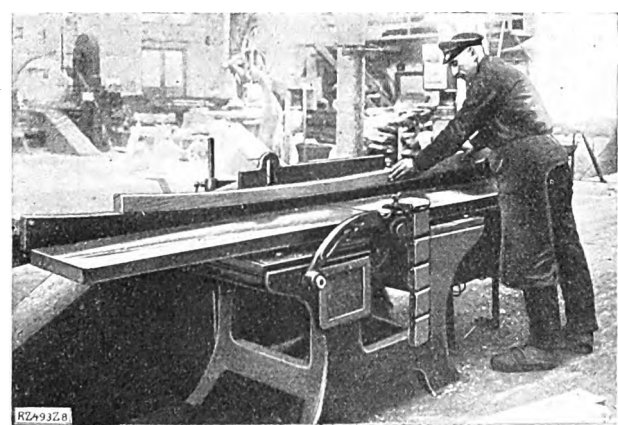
Abrichten des äußeren Bogens des Dachspriegels auf der Fräsmaschine
